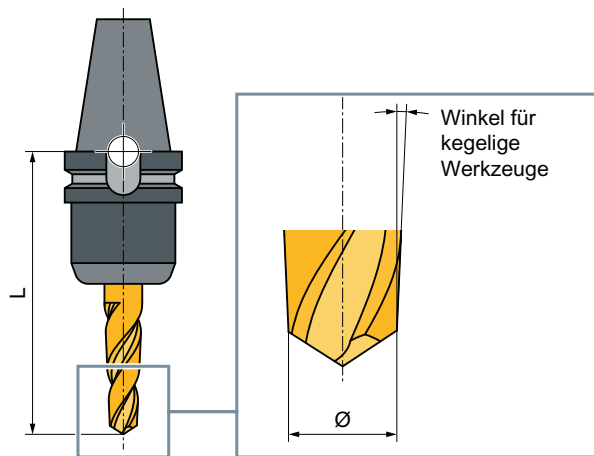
3D-Werkzeugtyp am Beispiel eines Kegelstumpffrsers (Typ 155)
